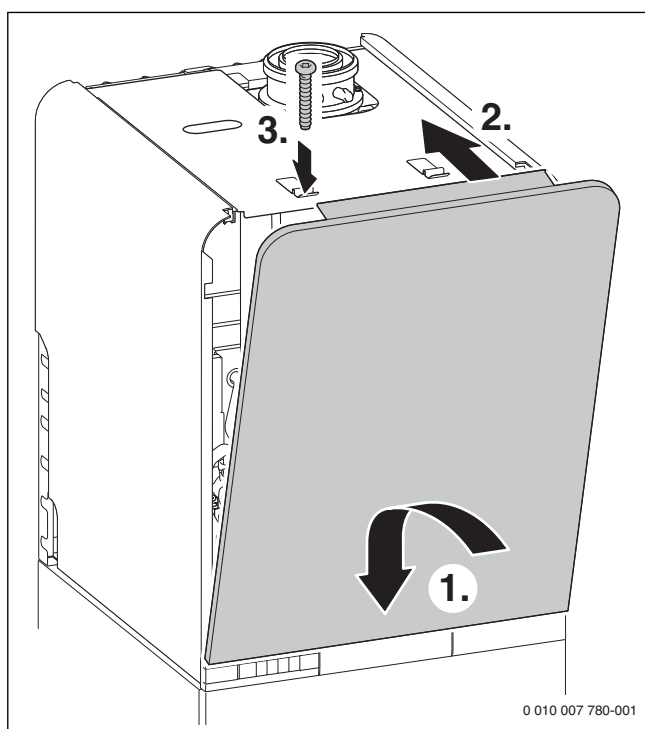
Posunutí horního opláštění dozadu a upevnění vpředu a vzadu 4 šrouby
